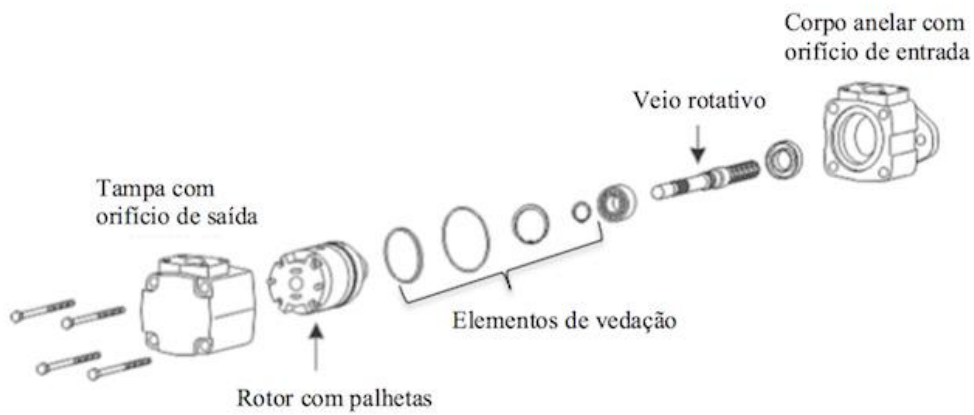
Bomba palhetas com vista explodida. [17]
